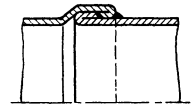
Muffenverbindung mit Schweißnahtentlastung.
